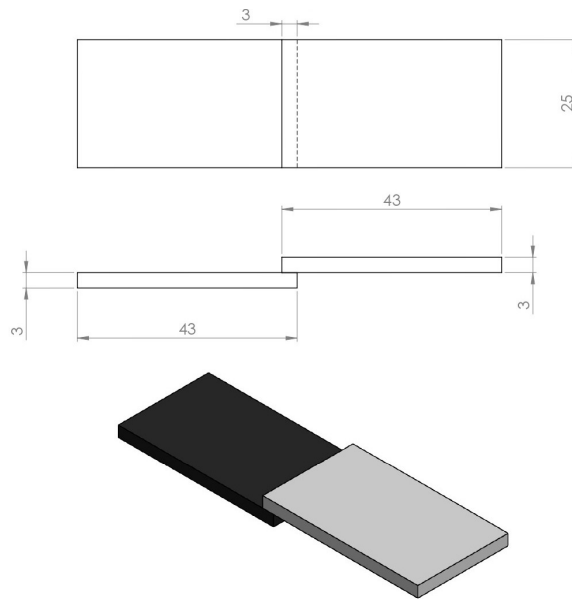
Desenho ilustrativo do pretendido para as juntas após soldadura laser
